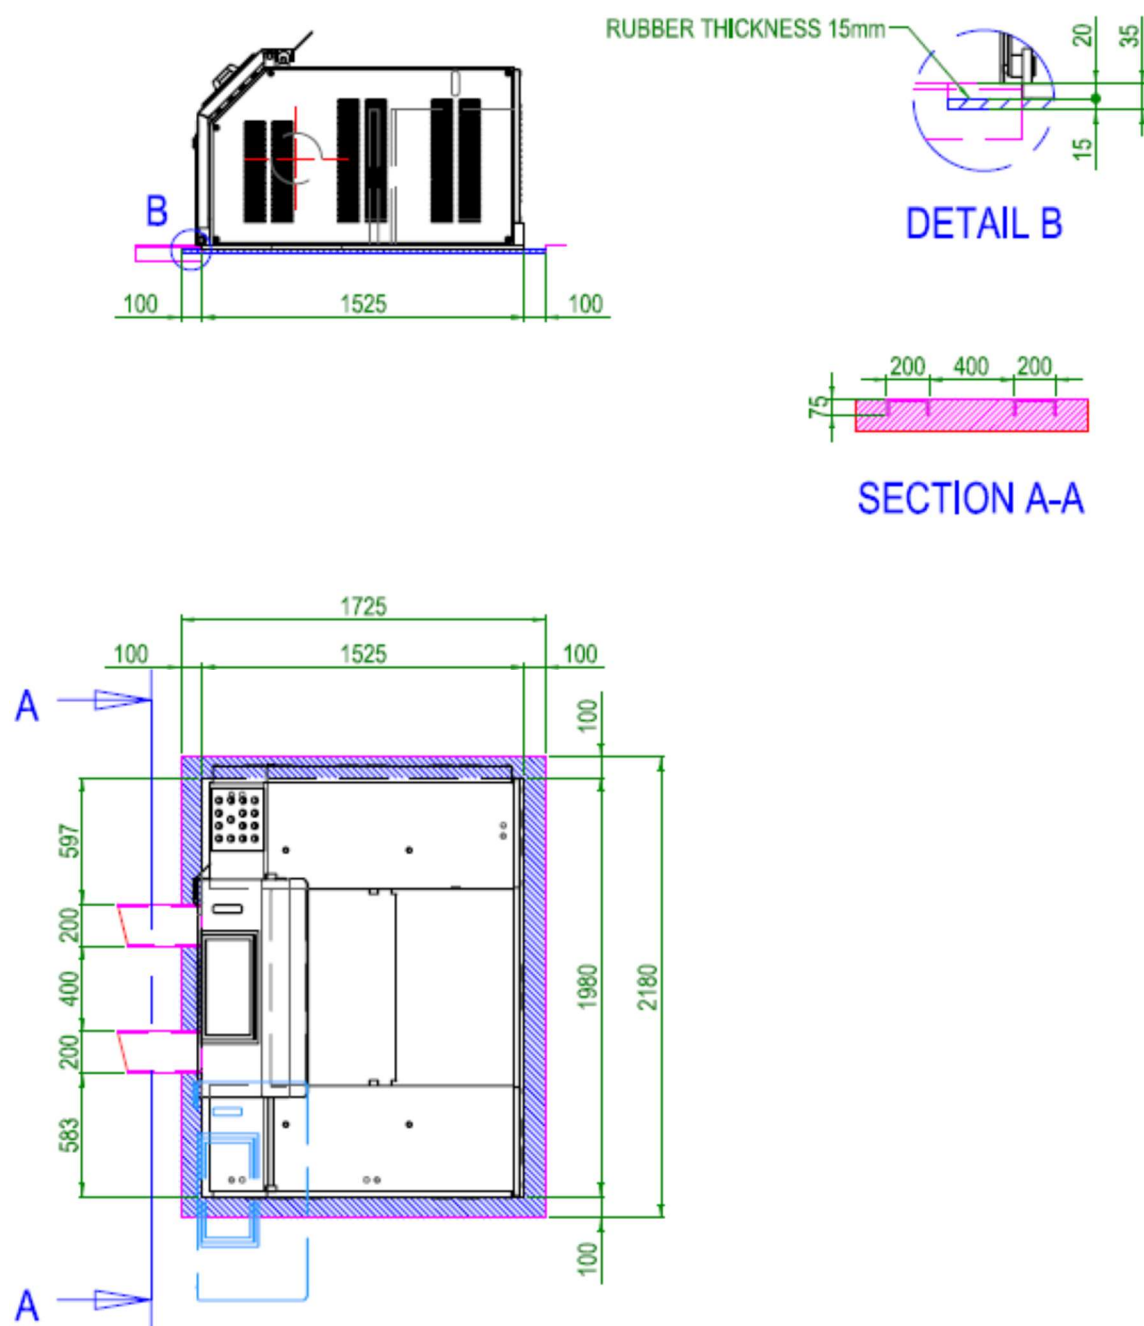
Layout da linha INF-4. Dimensões de instalação do desbobinador padrão.
